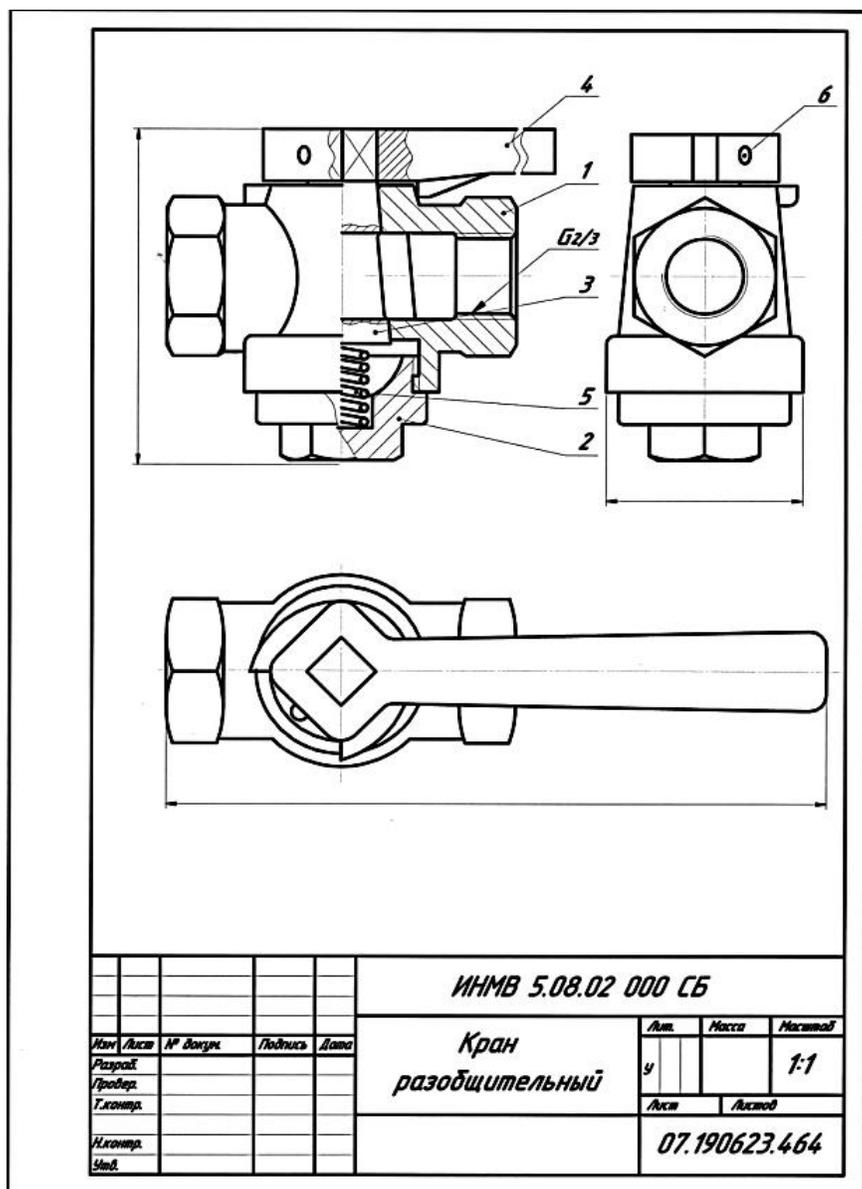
Образец сборочного чертежа для самостоятельной работы № 6 (вариант 2)
